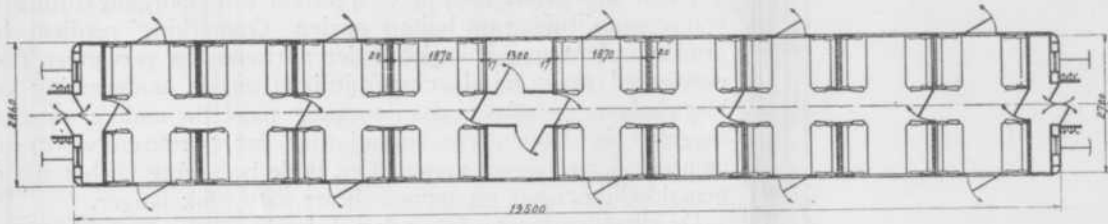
Coupérijtuig 3e klasse met doorgang en vouwbalgen. (Nord Français).
